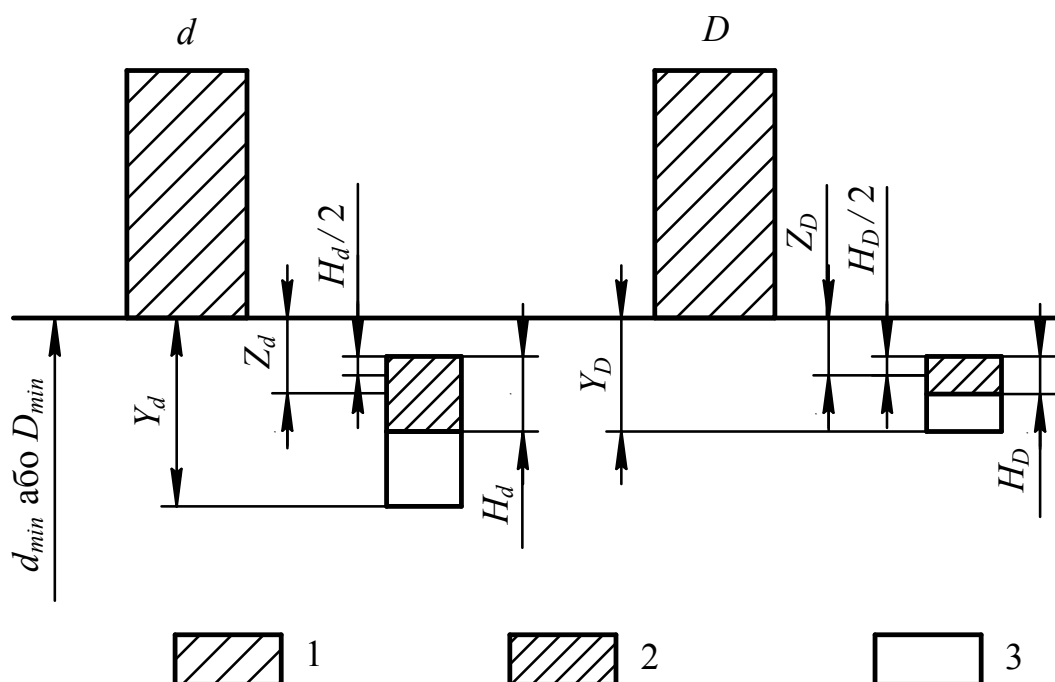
Розташування полів допусків: 1 – діаметра, що центрує, d або D втулки; 2 - на виготовлення калібра-пробки; 3 - поле зносу калібра-пробки
